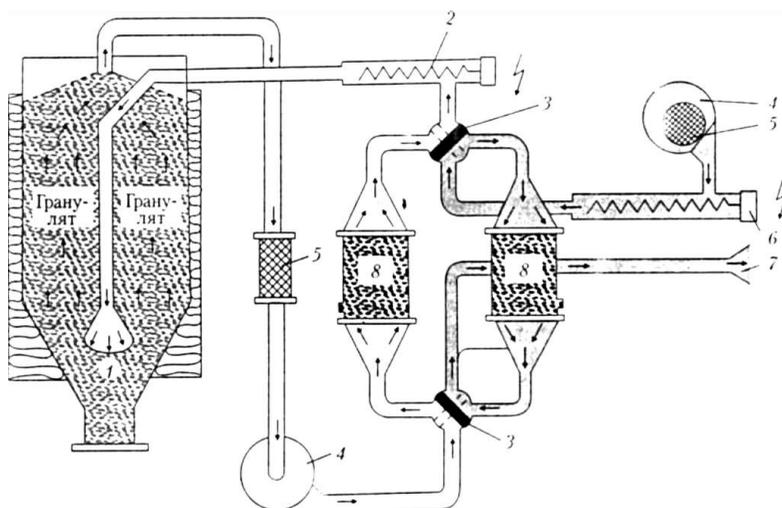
Бункерная сушилка: 1 – форсунка для выхода воздуха; 2 – теплообменник; 3 – разделитель; 4 – вентилятор; 5 – микрофильтр; 6 – нагреватель воздуха; 7 – вытяжная магистраль; 8 – резервуар для осушителя [16]
